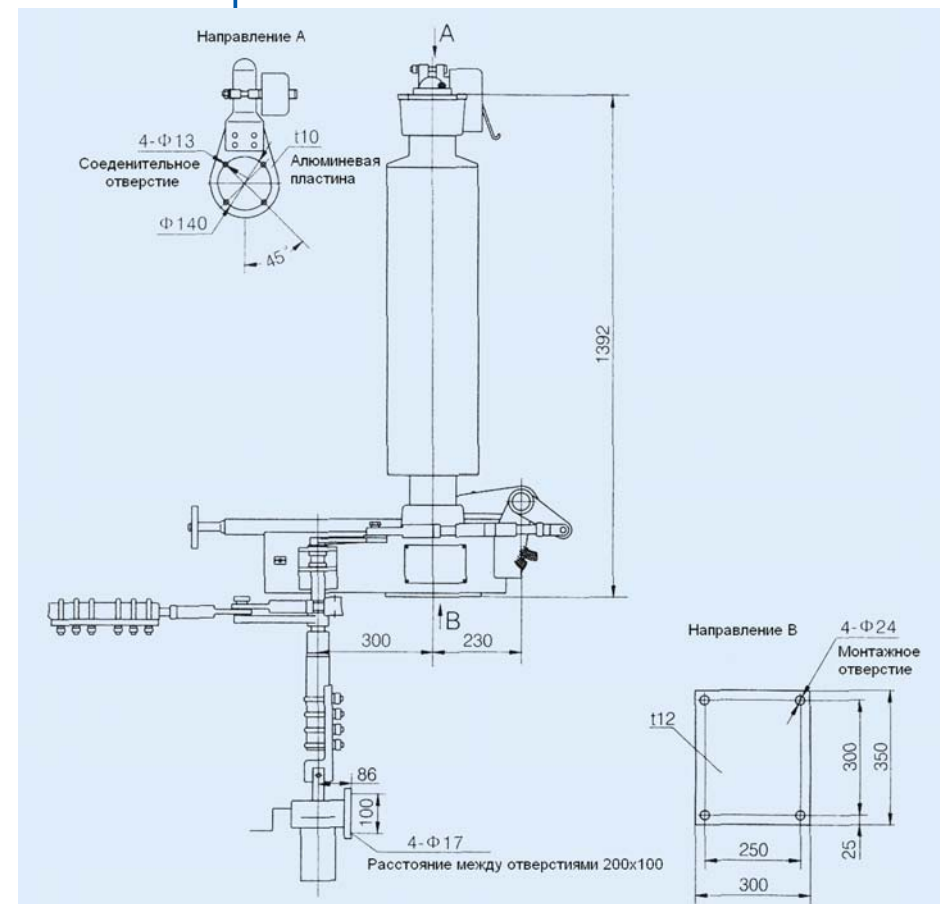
Внешний вид и размеры заземлителя JW□-126
